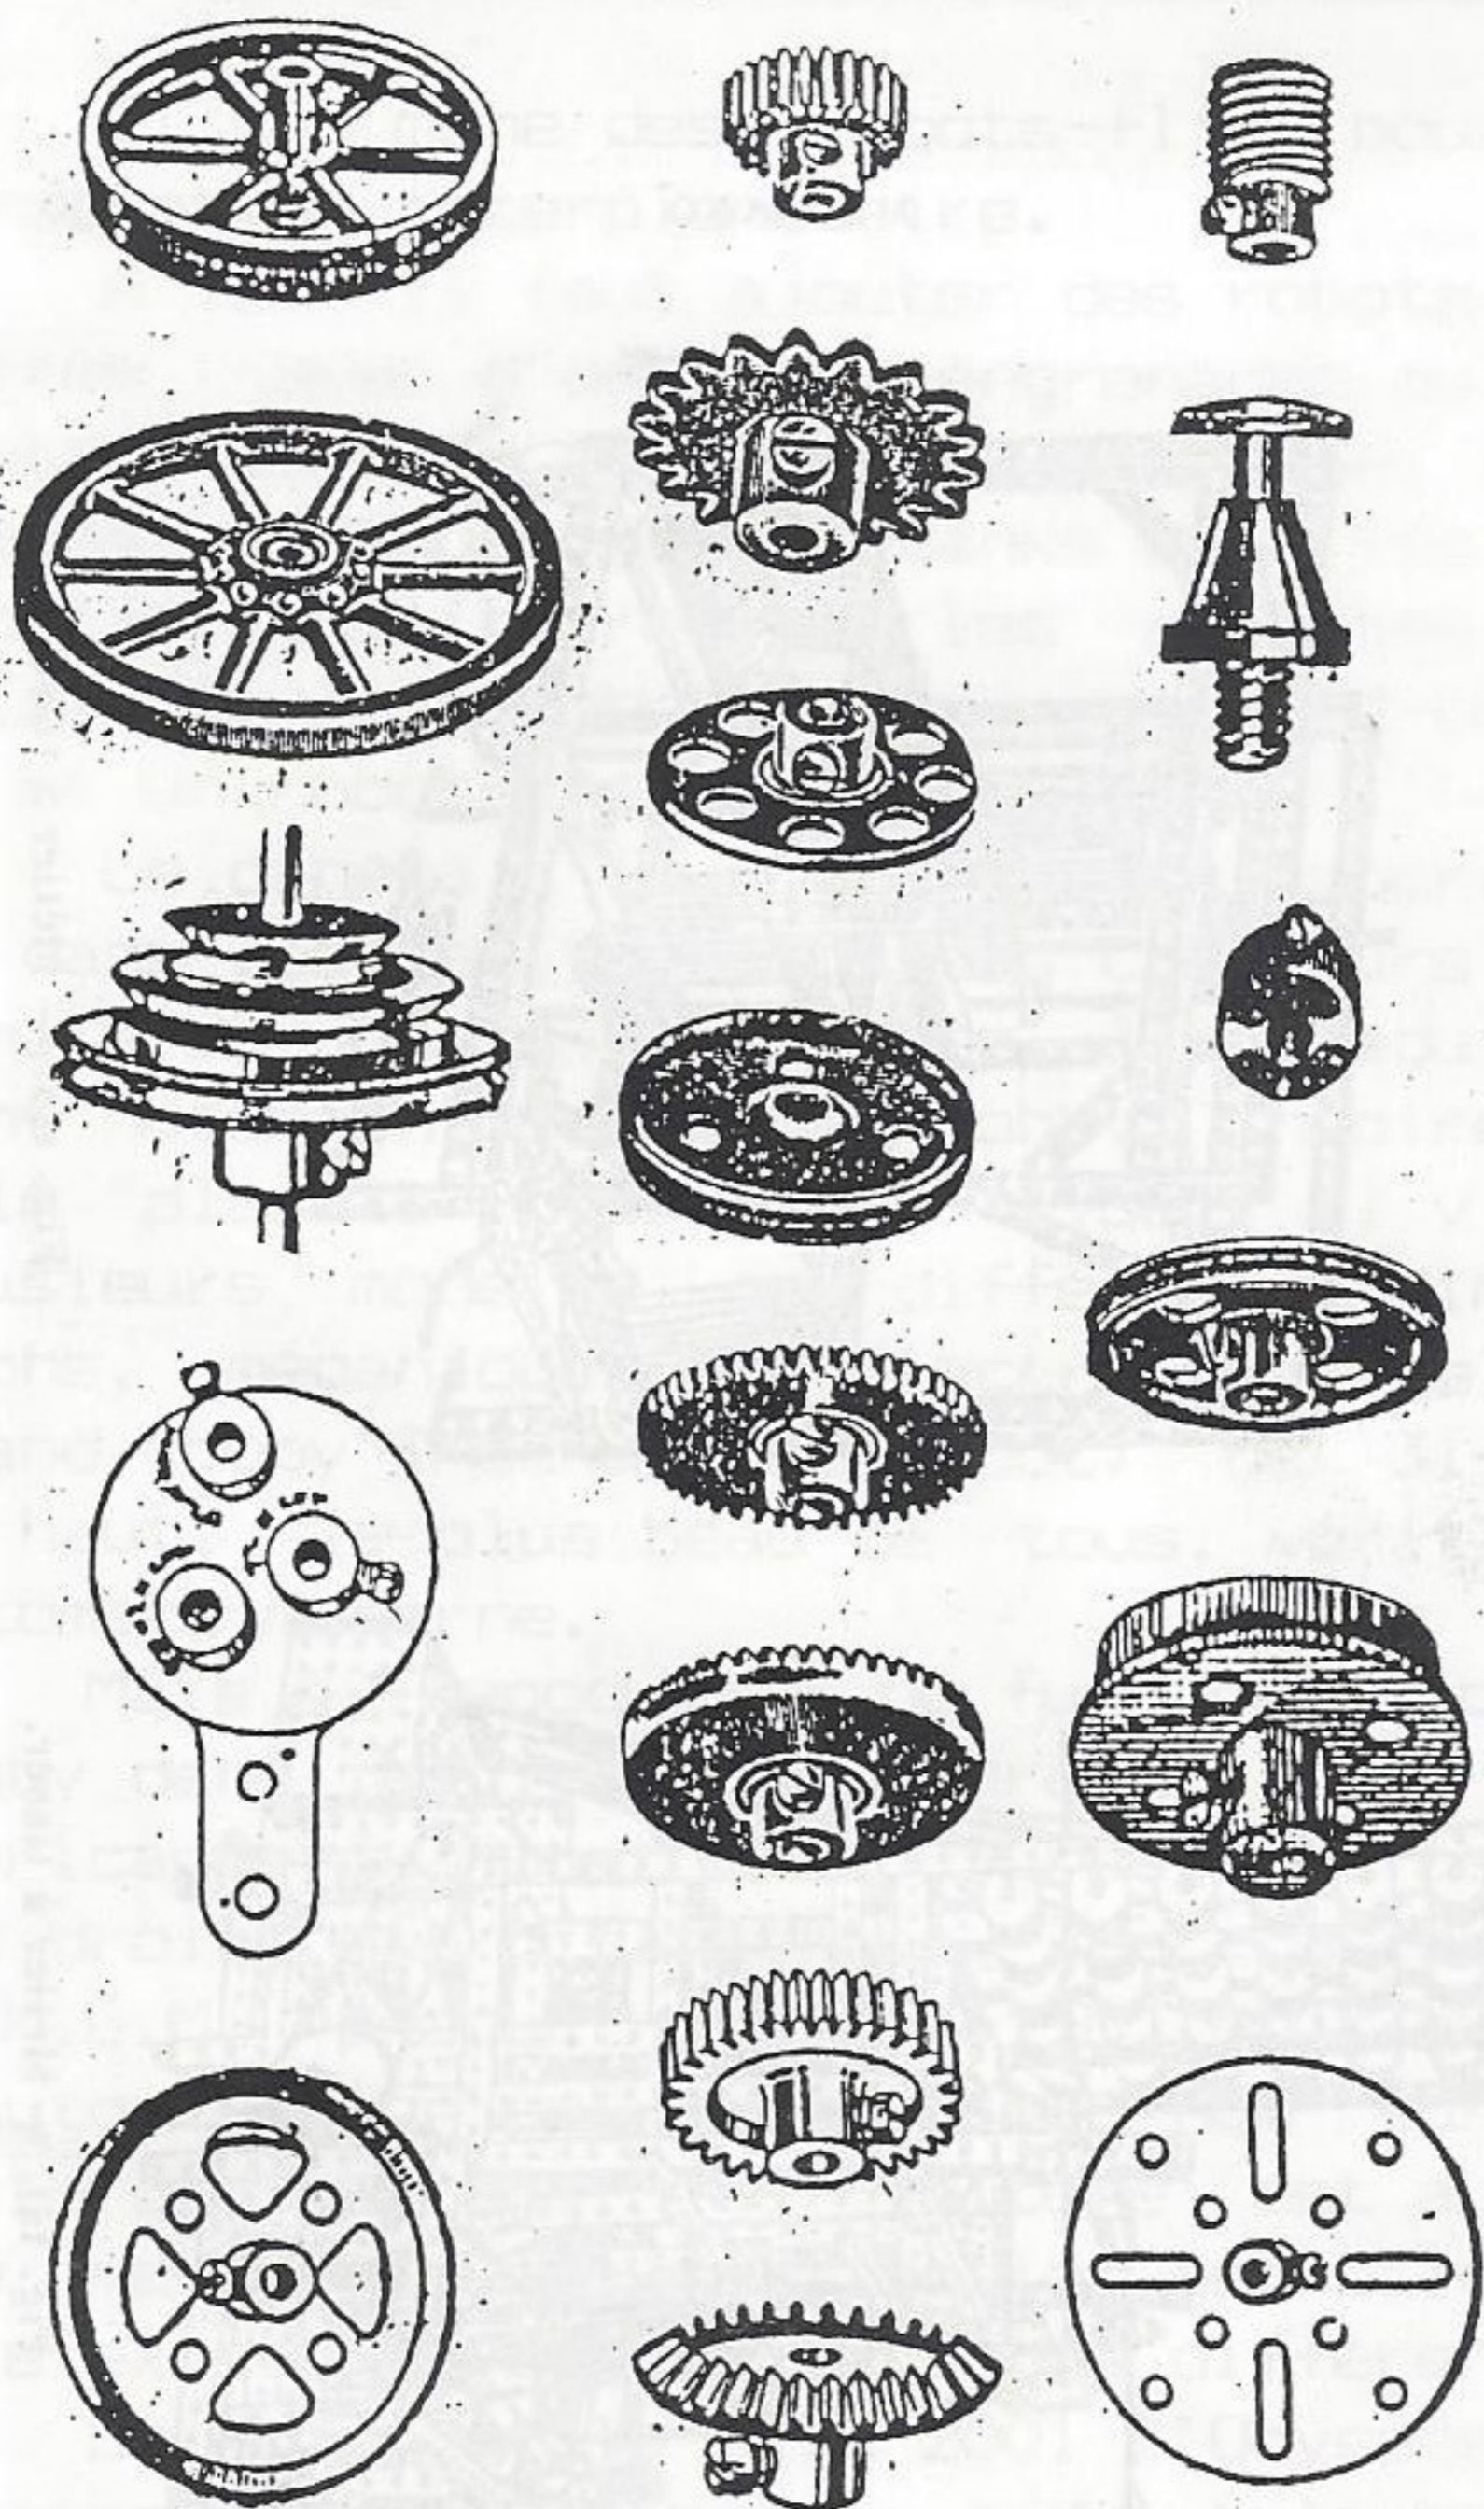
à 109. — Pièces détachées : roues, engrenages, plateau central, vis sans fin.
